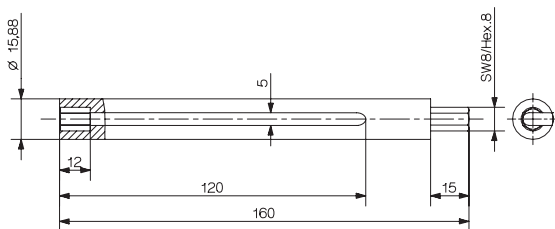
Montageschlüssel für tiefe Bohrungen Typ 1300A41
